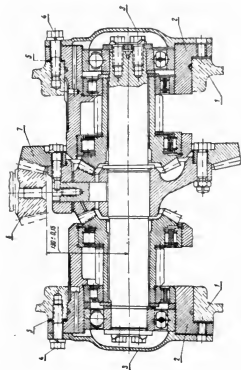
Регулировка центральной (конической) передачи трактора «Беларусь»:
